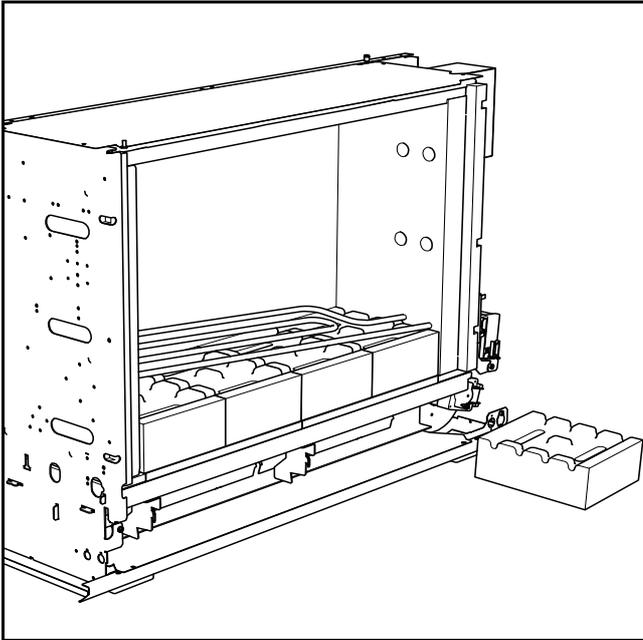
Heizkörper durch die Öffnungen der Seitenwand-Wärmedämmung einschieben.
